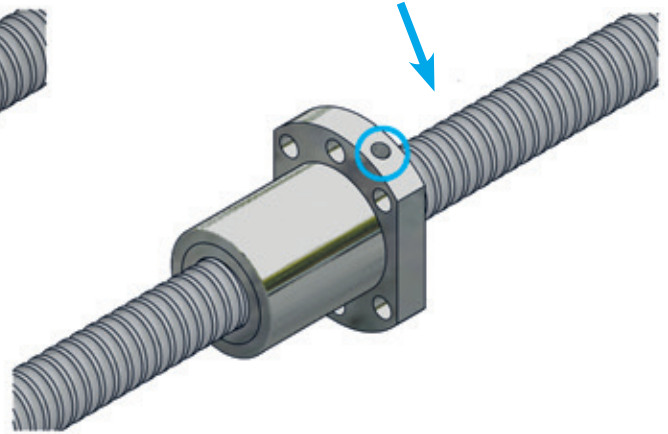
Flanschnuttermutter mit Gewindebohrung
